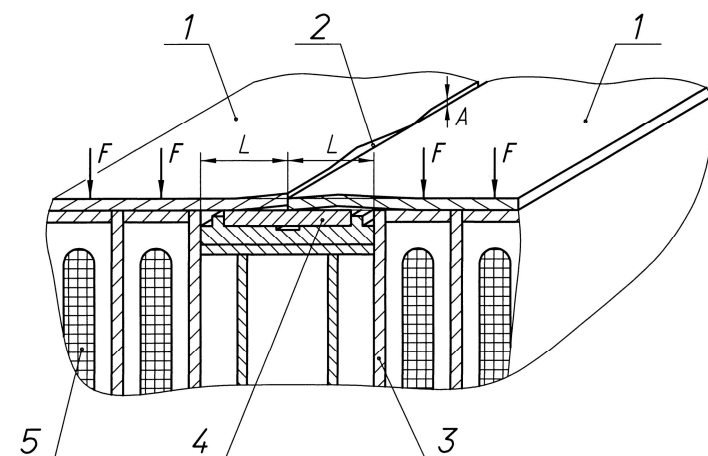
Схема сборки сварного стыка листового полотнища на электромагнитном стенде с медными подкладками
